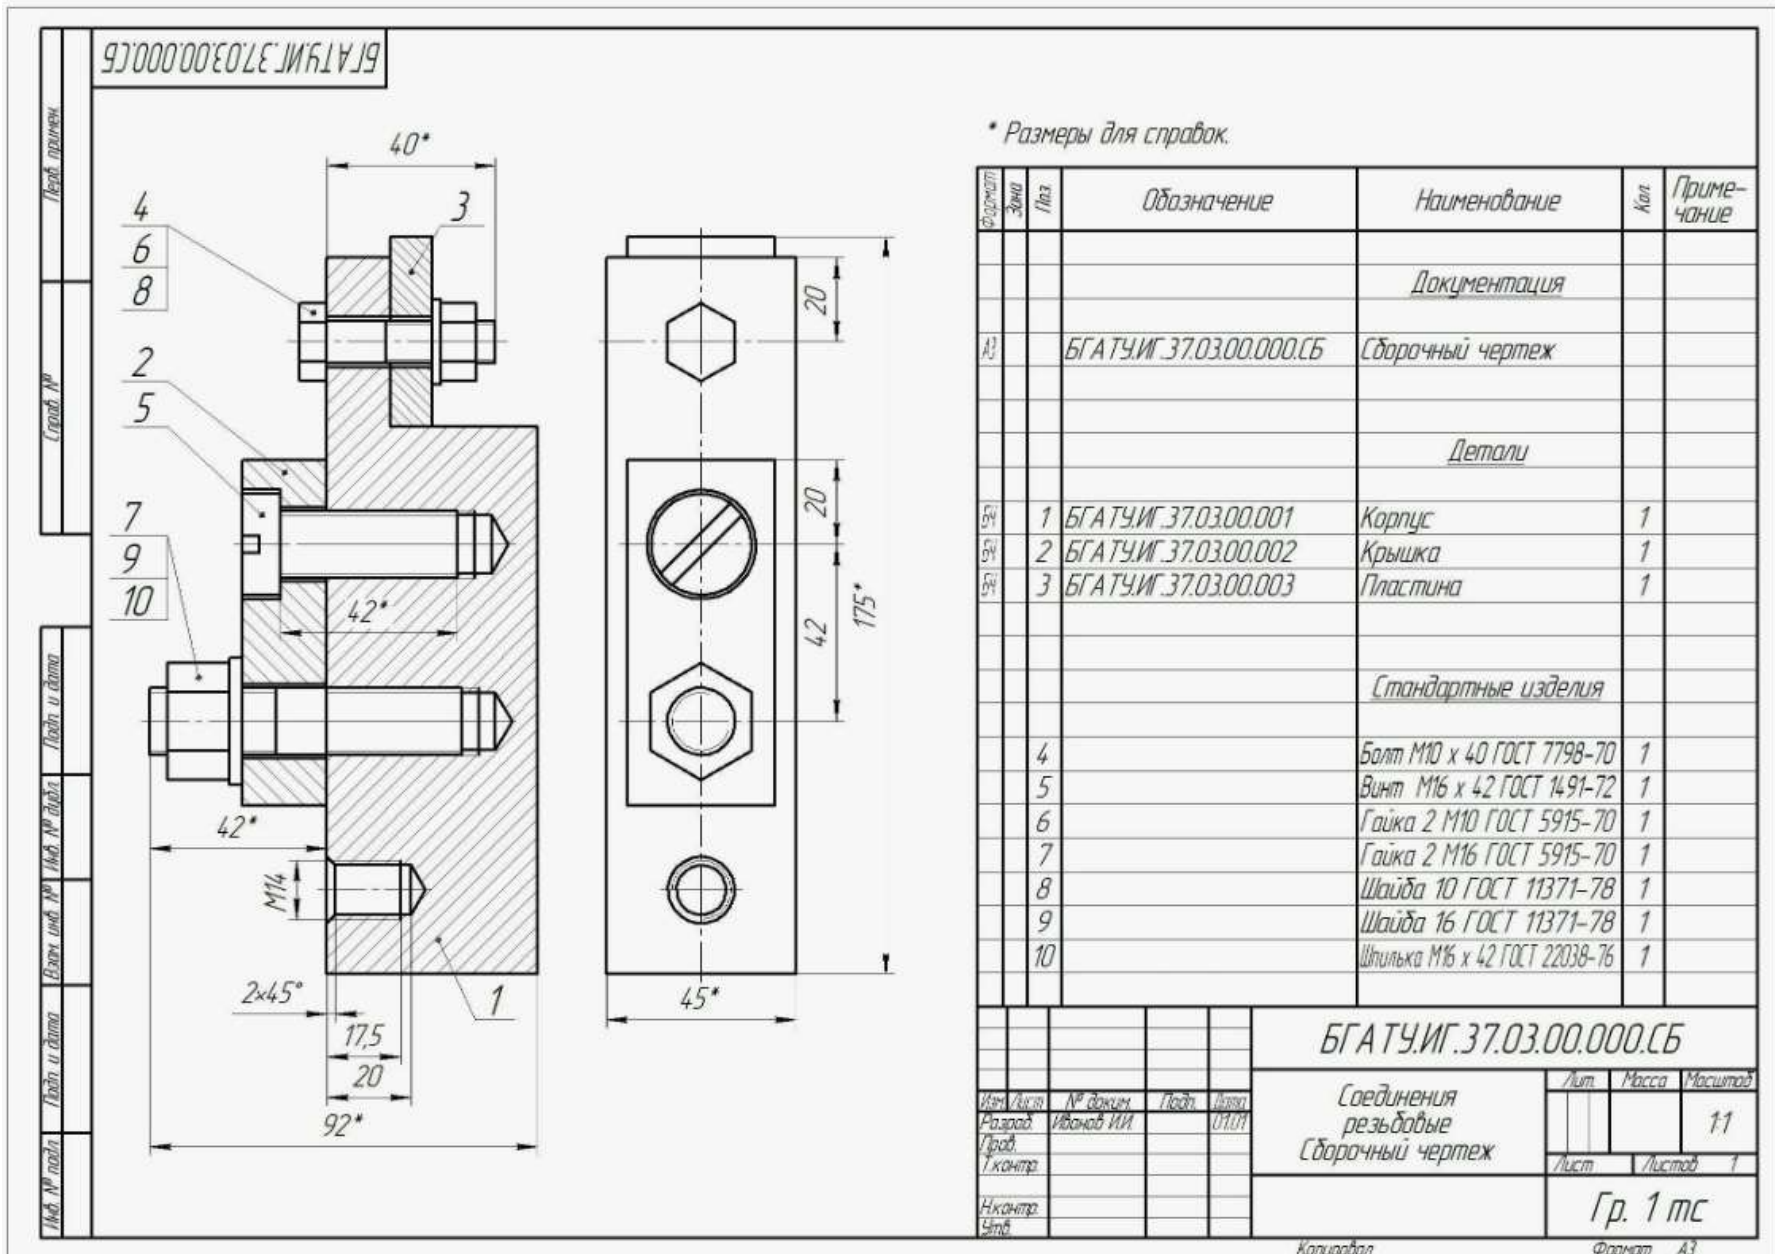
Пример ошибок при подготовке сборочного чертежа
